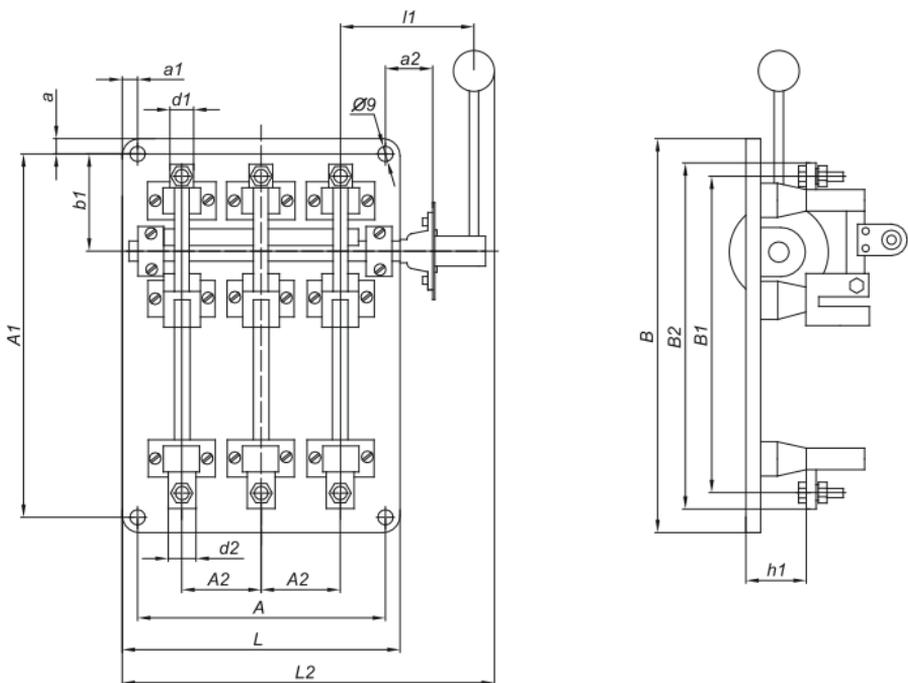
Размеры разъединителей-предохранителей РПБ
